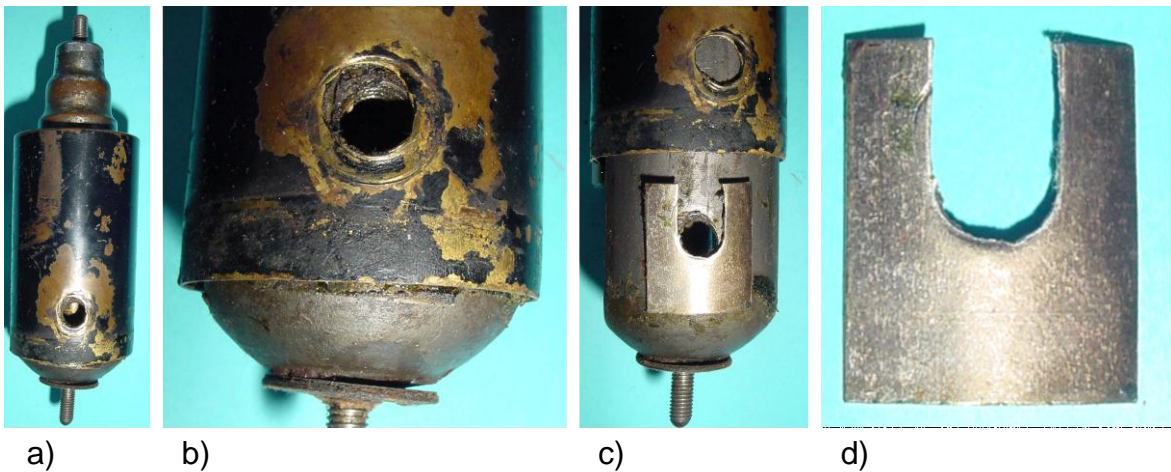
Befestigung des Drehbolzens: a) Bohrung im Gehäusemantel, Gewindebohrung im Magneten, c) hochgeschobener Gehäusemantel, d) Stabilisierungsblech
